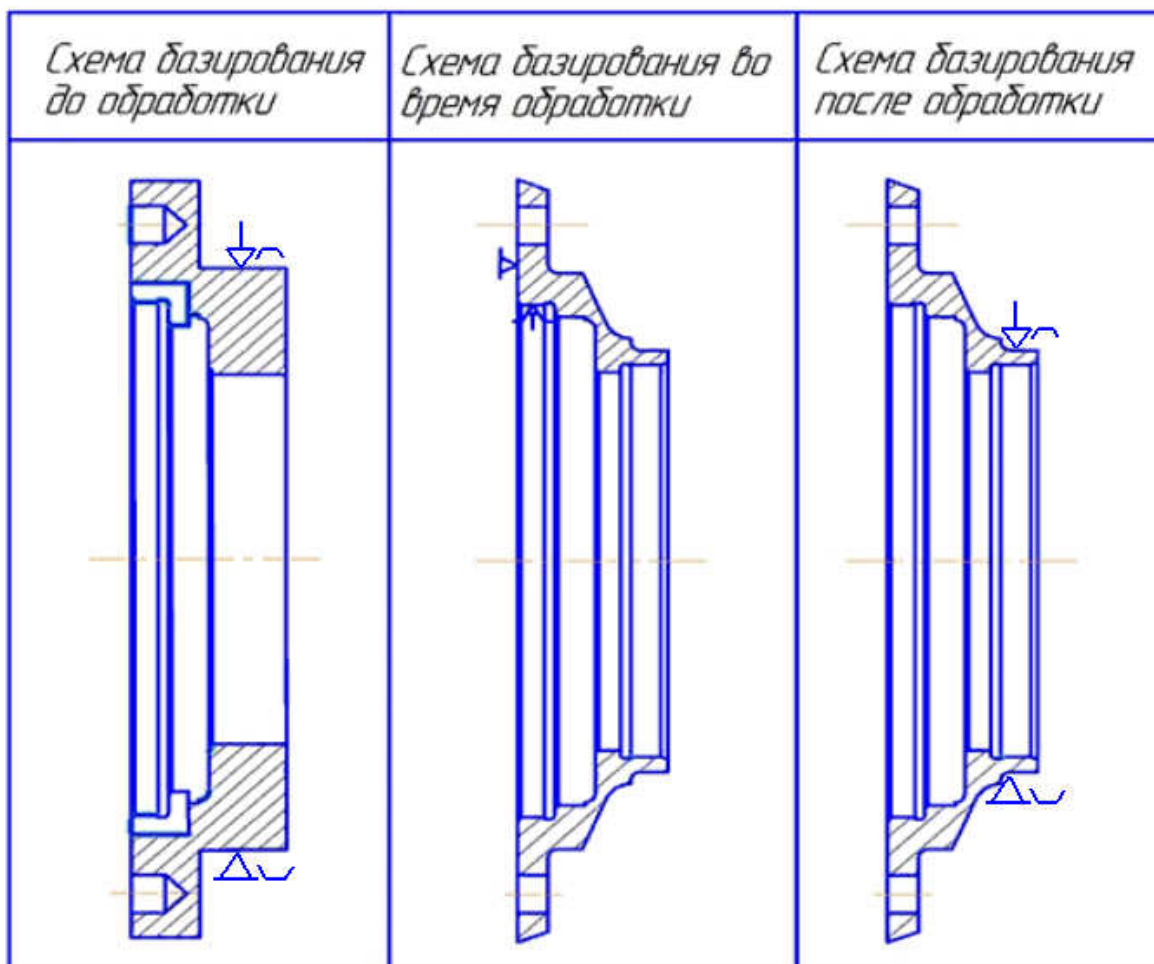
Схема базирования заготовки на 010 комплексной операции с ЧПУ
